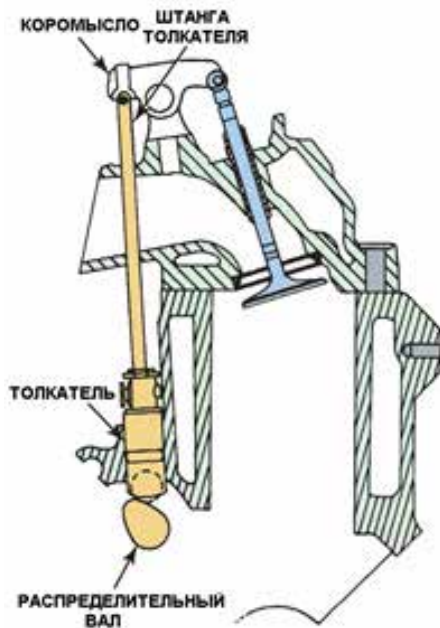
Двигатели с верхним расположением клапанов (ОНВ) оснащены длинной штангой толкателя, который передает движение от толкателя к коромыслу; источник: *Pearson Education, Inc.
